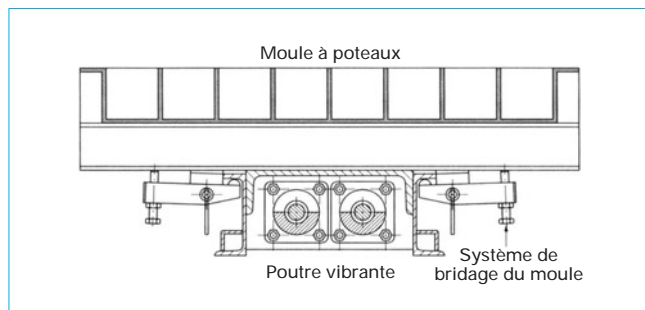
Coupe d'un moule à poteaux de clôtures bridé sur sa poutre vibrante
